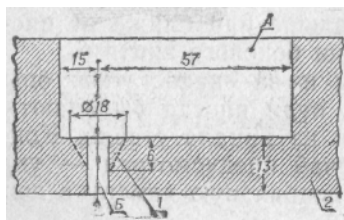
Доработка выводного канала для провалившихся пуль из камеры ложи пневматической винтовки «312» (ГДР):
